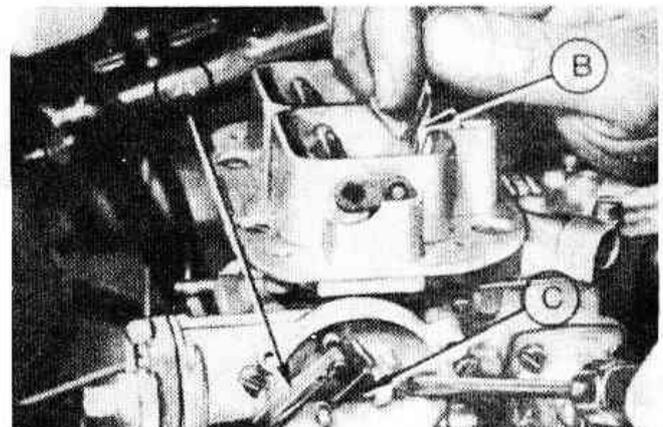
Резиновая лента (A), сверло (B) и тяга (C) (Разд.28)
